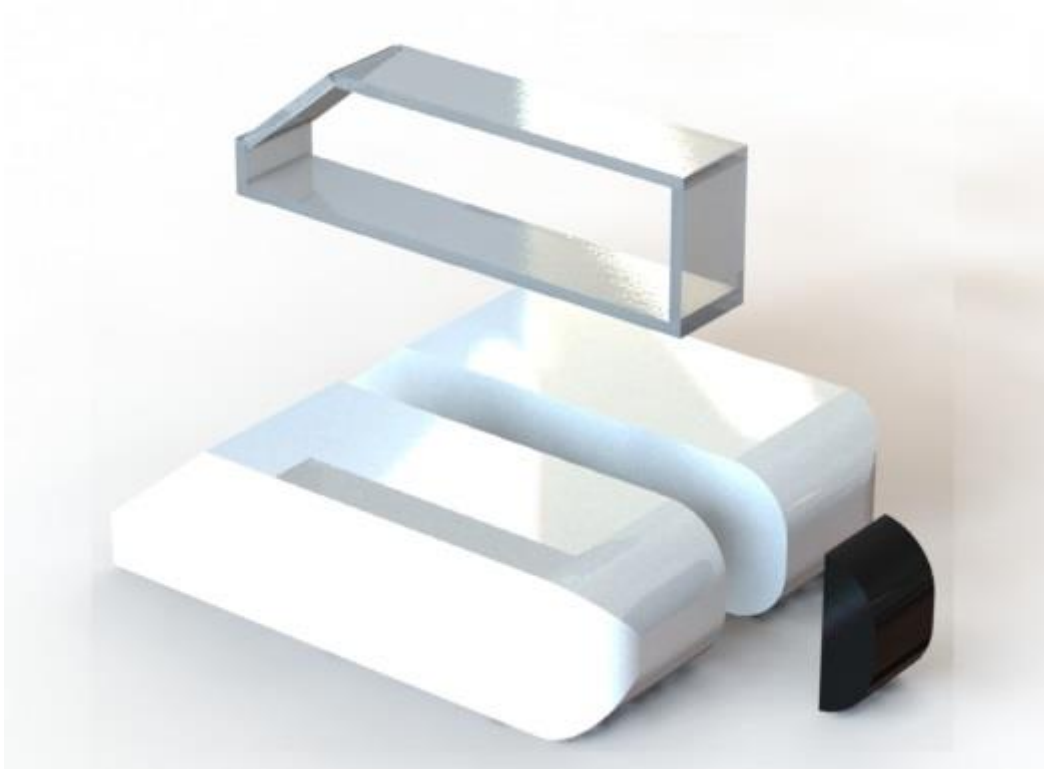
Render da vista explodida dos segmentos do corpo fabricado.
